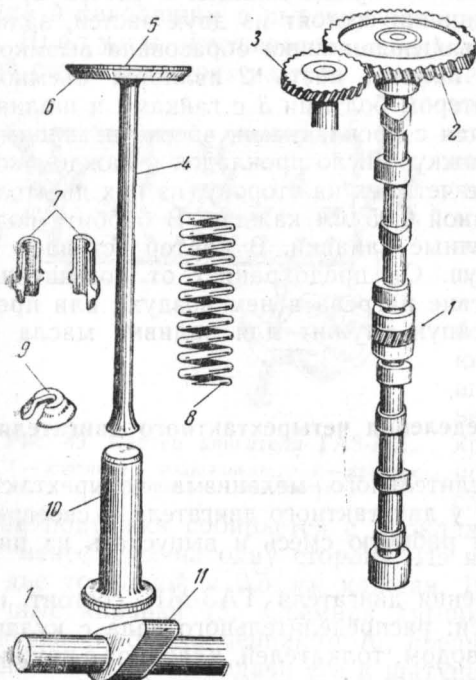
Детали газораспределительно-го механизма двигателя ГАЗ-МК:
